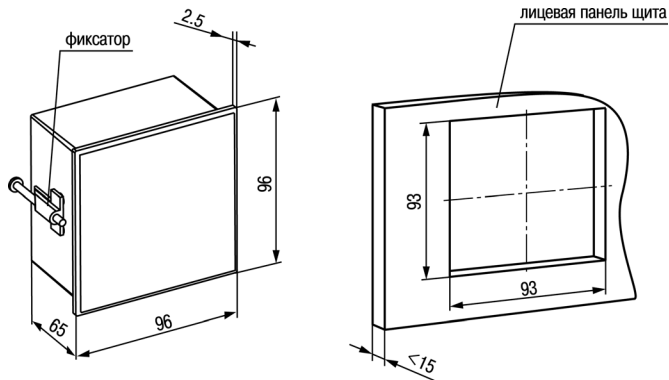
Габаритные размеры корпуса Щ1
